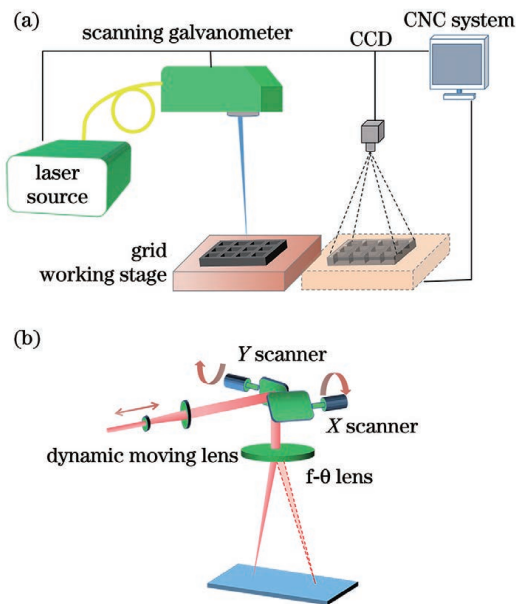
焊接装备组成及动态聚焦扫描振镜原理示意图。
